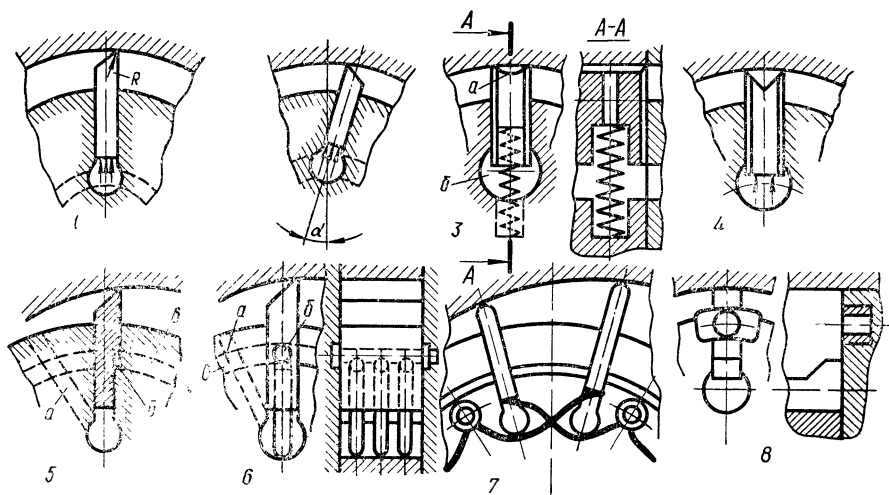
Конструкция пластин и способ встройки их в ротор машины пластинчатого типа
